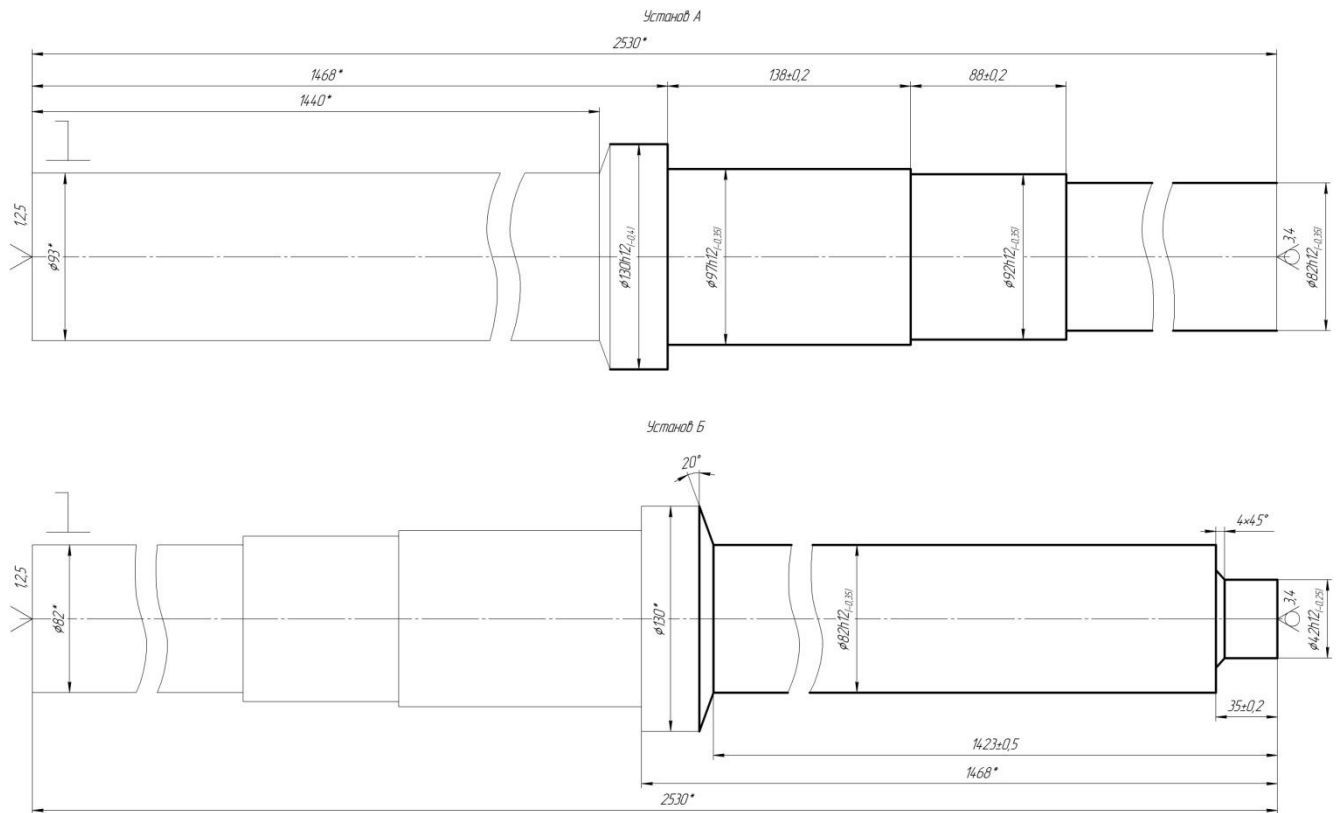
Схема базування заготовки на токарній з ЧПК операції (другий варіант)
